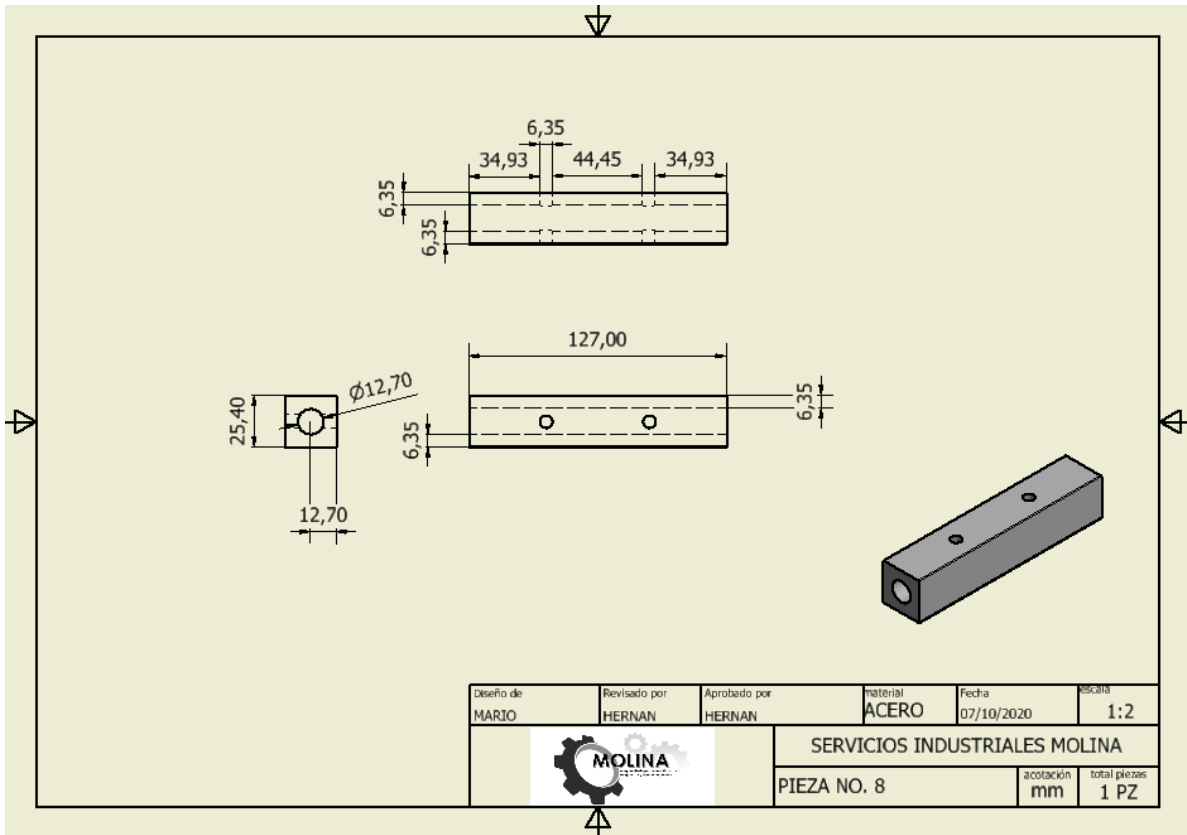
plano de pieza secundaria de apoyo para barrenos.
